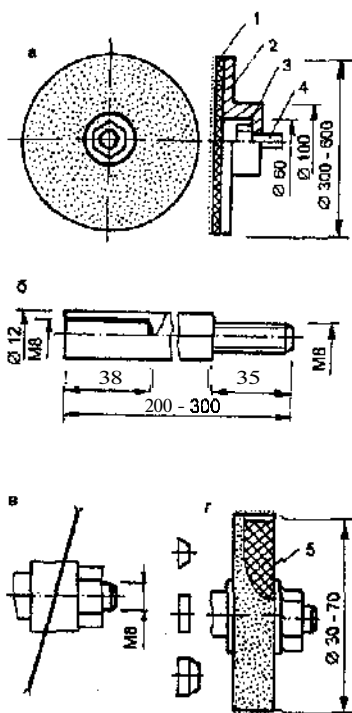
Приспособления для механизированной обработки древесины: а — диск для шлифовки плоскостей больших размеров; б — насадка-удлинитель, в — пьюная пила, г — валики цилиндрической, конической и цилиндрическо-конической форм для шлифовки вогнутых поверхностей: 1 — шлифовальная шкурка, 2 — диск из алюминия или фанеры, 3 — гайка, 4 — вал, 5 — микропористая резина
